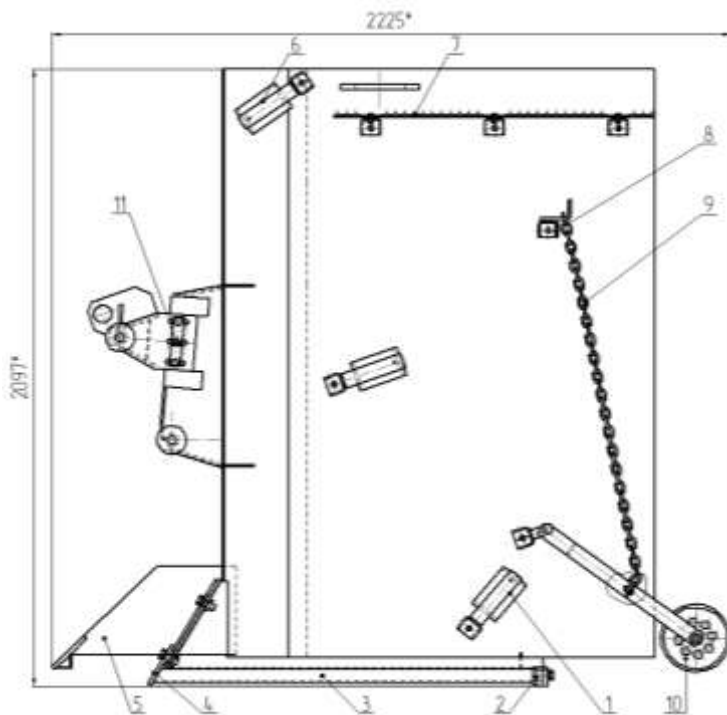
Трубоукладчик для укладки пластмассовых труб: 1 и 6 – направляющая; 2 – носовина; 3 – угольник; 4 – нож; 5 – очиститель; 7 – решетка; 8 – стяжка; 9 – цепь; 10 – прижимной ролик; 11 – болт
